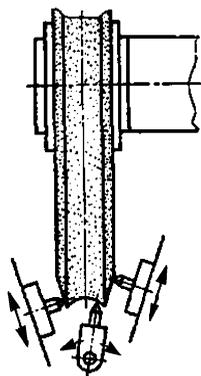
Схема правки шлифовального круга алмазами с помощью приспособления для правки
